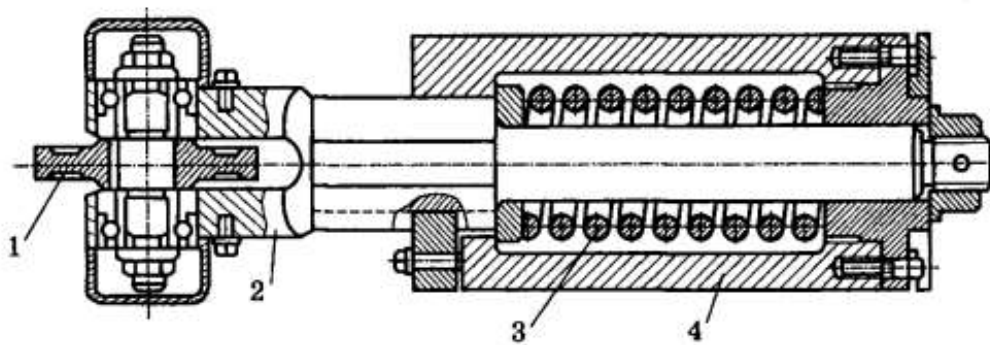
Пристрій для обкатки зовнішніх циліндричних поверхонь
